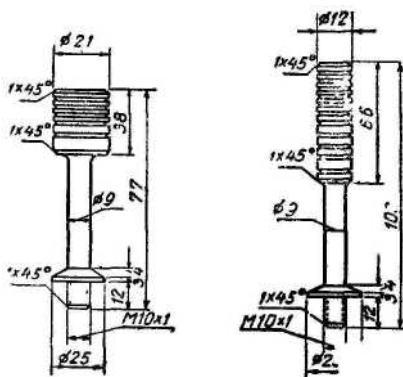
Рабочий чертеж штоков второй и третьей ступени
